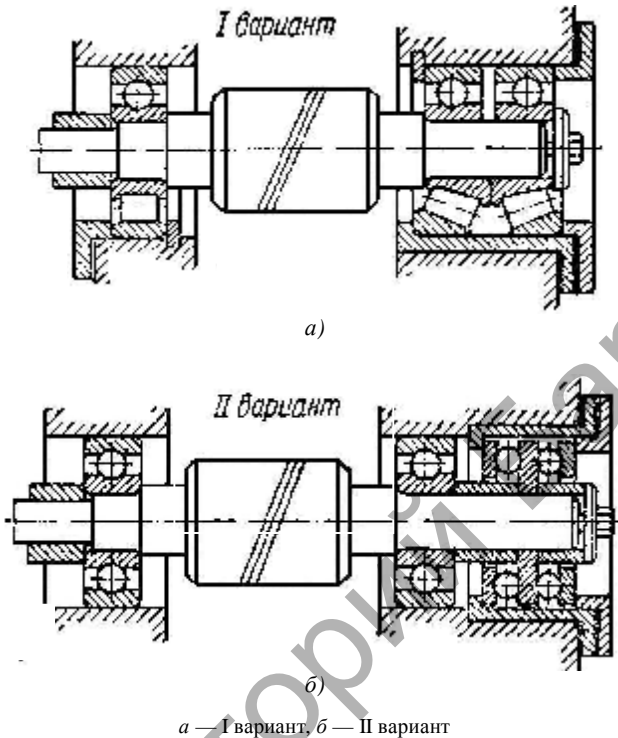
Схемы подшипниковых узлов червячных редукторов
